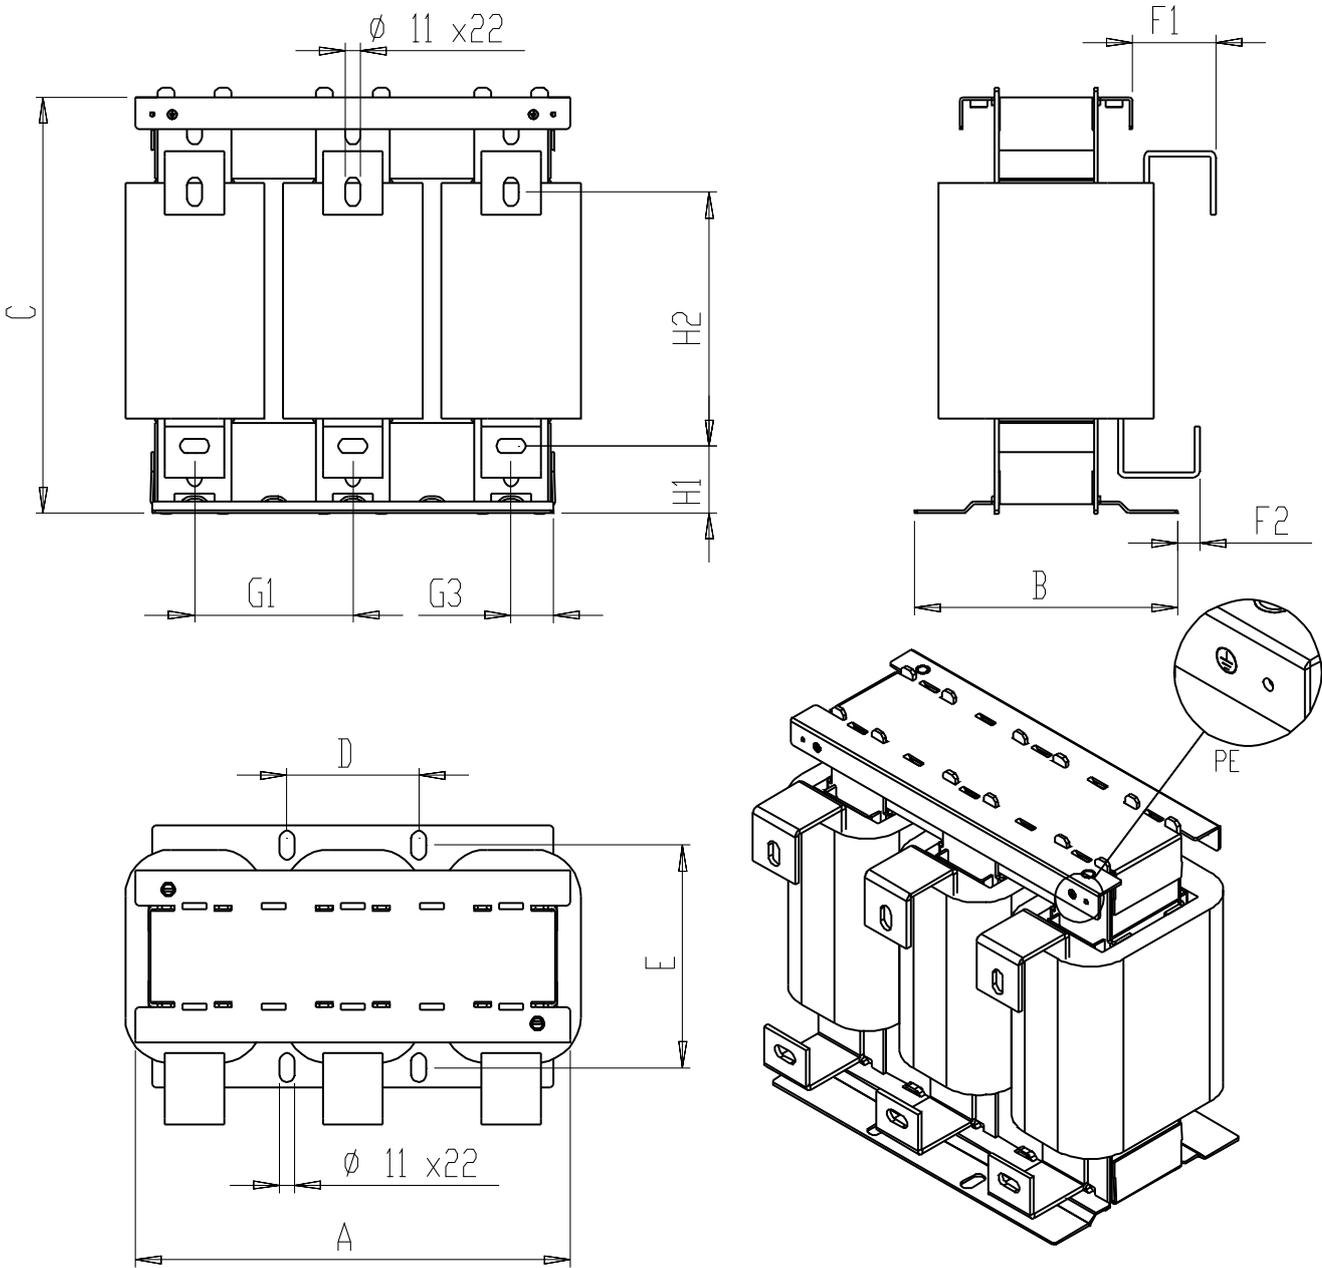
Disegno quotato bobina di rete 6SL3000-0EH34-7AA0
